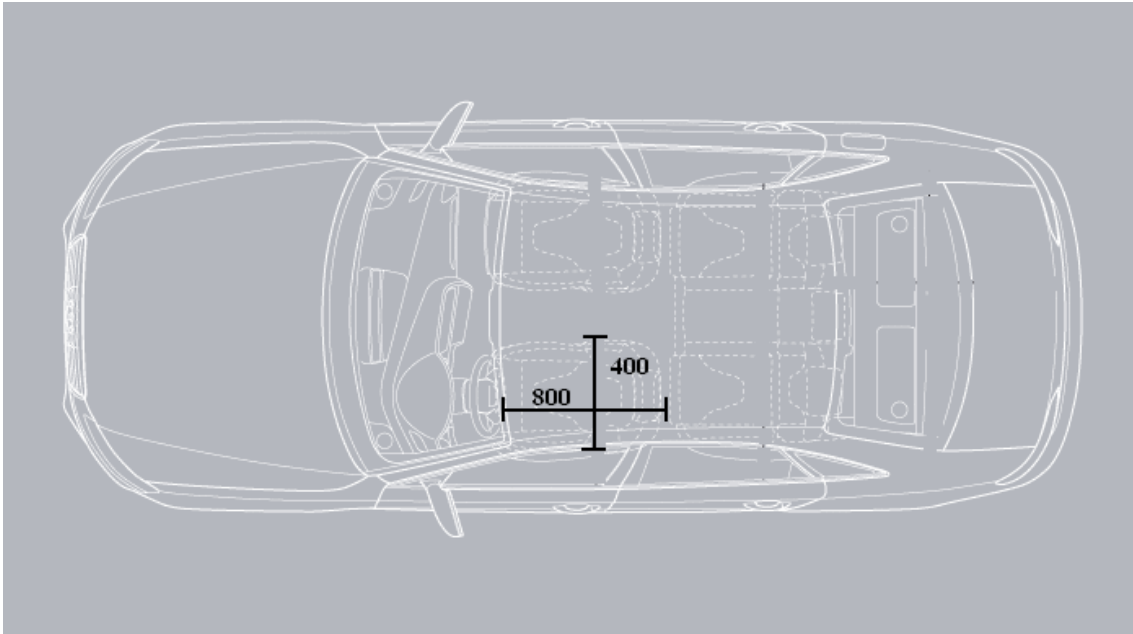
Vista en planta Audi A4. Dimensiones de alojamiento
